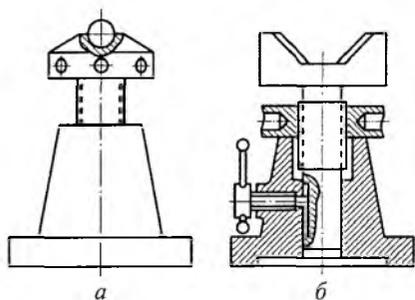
Домкраты с шаровой (а) и призматической (б) опорой для заготовки
